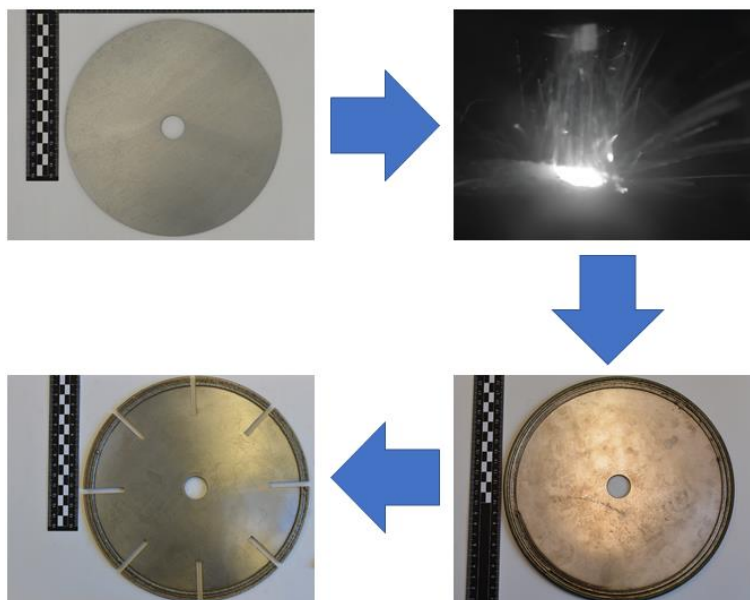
Prozesskette der CAMG-Scheibe beginnend beim Rohling, dem anschließenden Schweißprozess und der finalen Bearbeitung mittels Wasserstrahlschneidens am Beispiel einer Elektrode aus S355JR + CoMo28Cr
